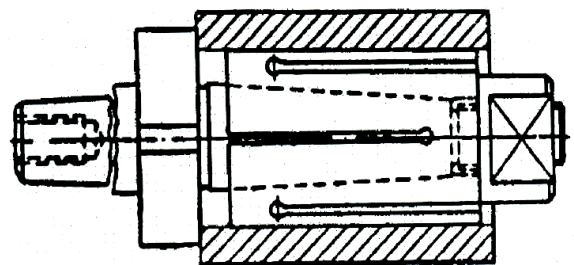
Установа заготовок на розтискній цанговій оправці
